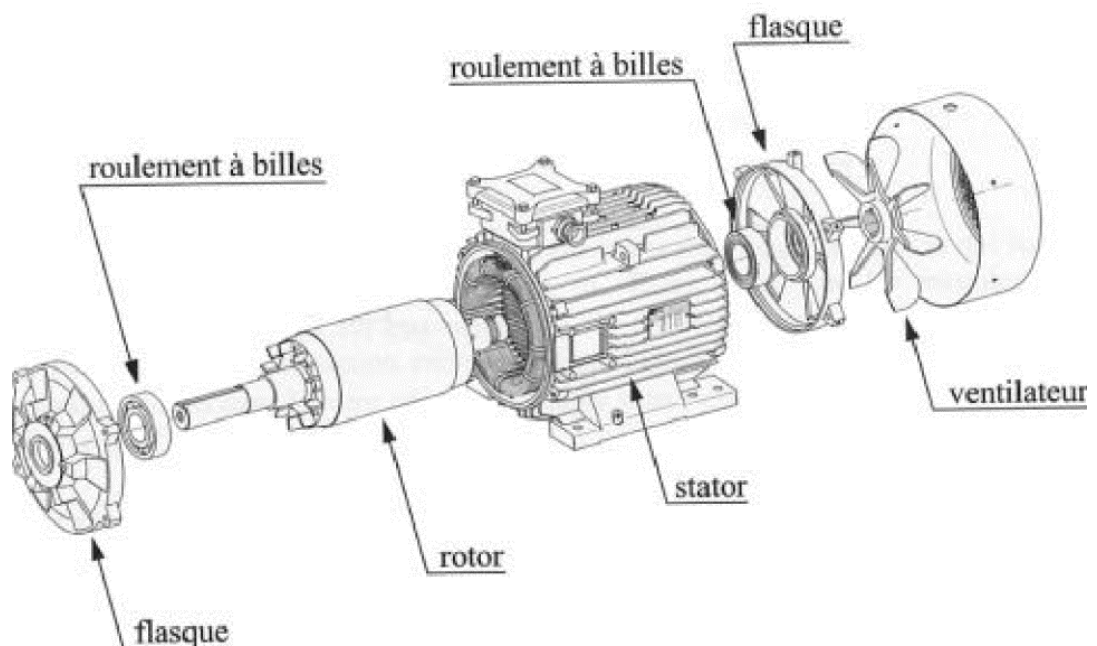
Structure d'une machine asynchrone à cage d'écureuil ou à rotor massif.
